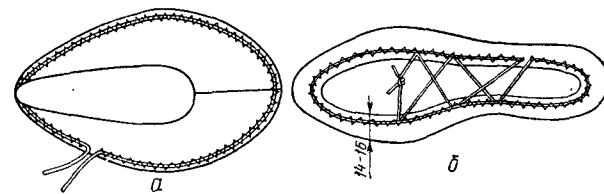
Схемы пристрачивания льняной нитки к заготовке верха (а) и шнуровочной затяжки (б)
